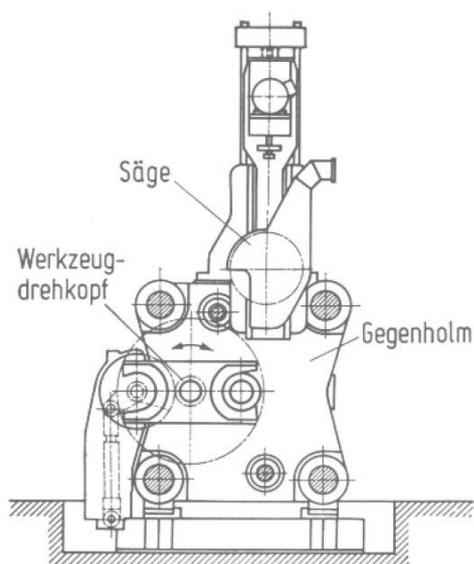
Werkzeugdrehkopf<sup>(Lange, S. 442)</sup>
